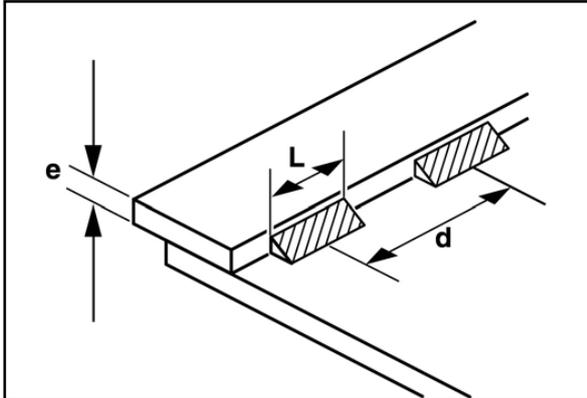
Relación grosor de chapa / distancia de los puntos de soldadura
